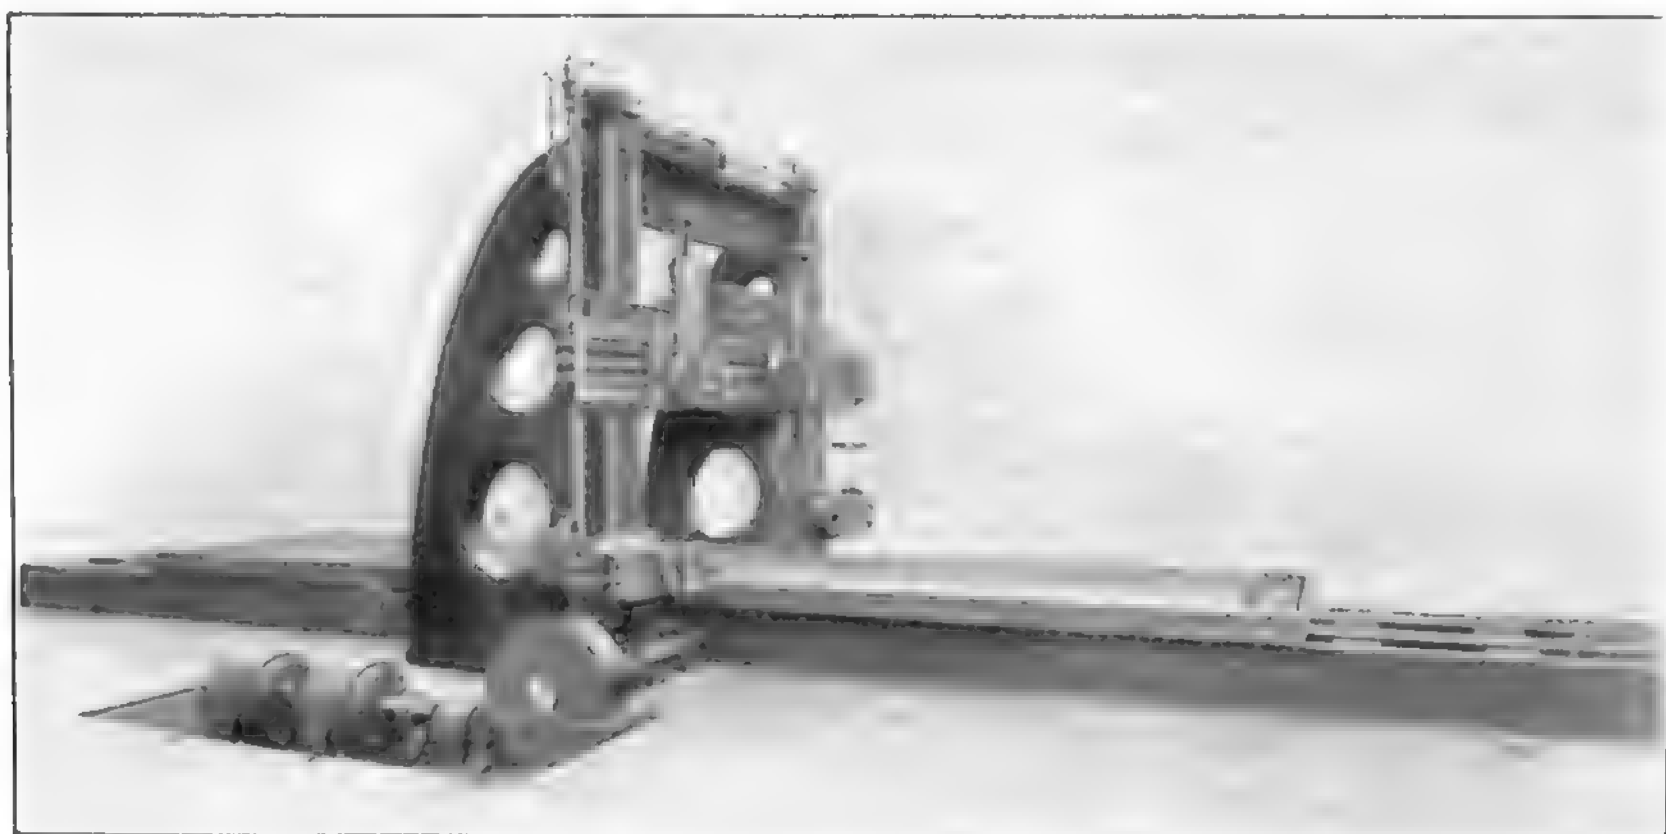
Hobelmaschine mit Umkehrreguliermotor.
